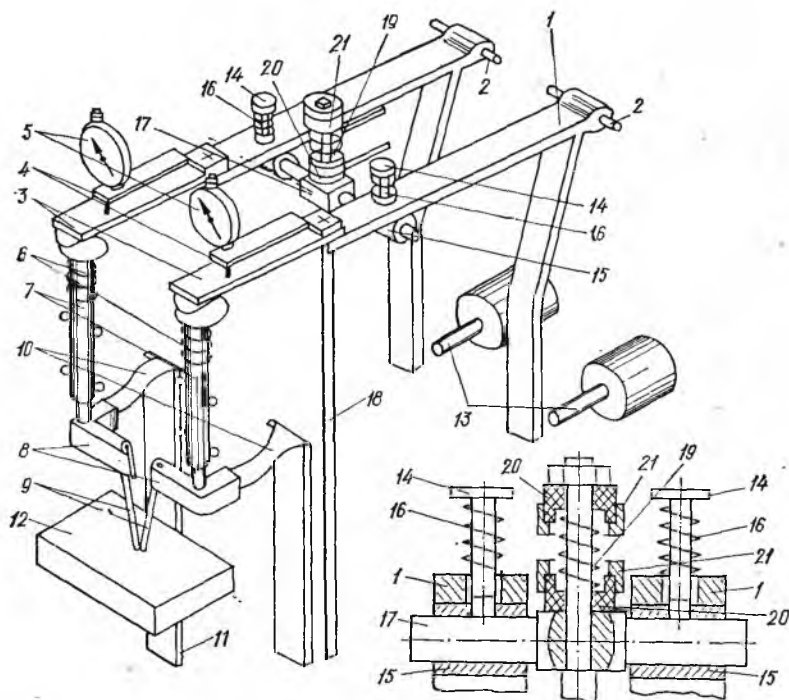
Кинематическая схема пружинного механизма сжатия электродов с педальным приводом для двухточечной сварки.
